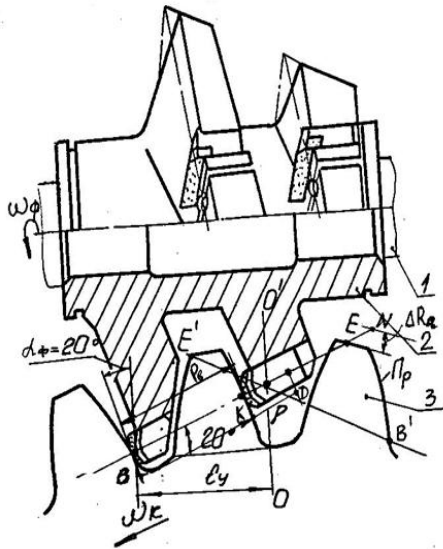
Схема верстатного зачеплення правого корпусу фрези і оброблюваного колеса
